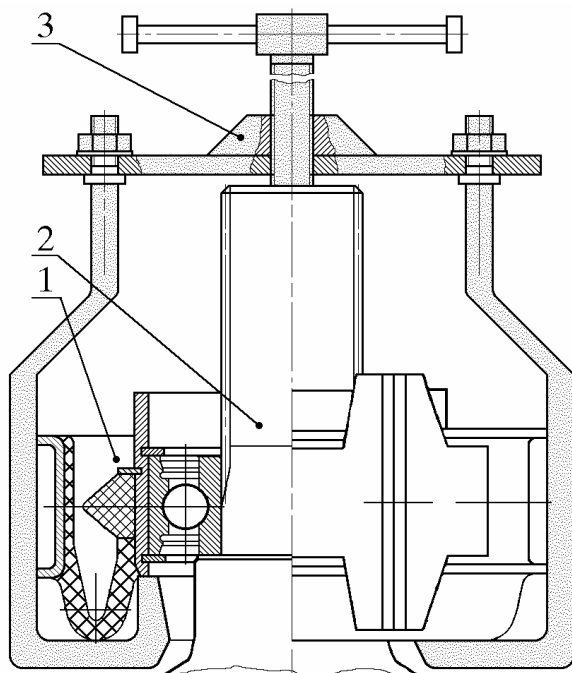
Выпрессовка промежуточной опоры с промежуточного вала:
